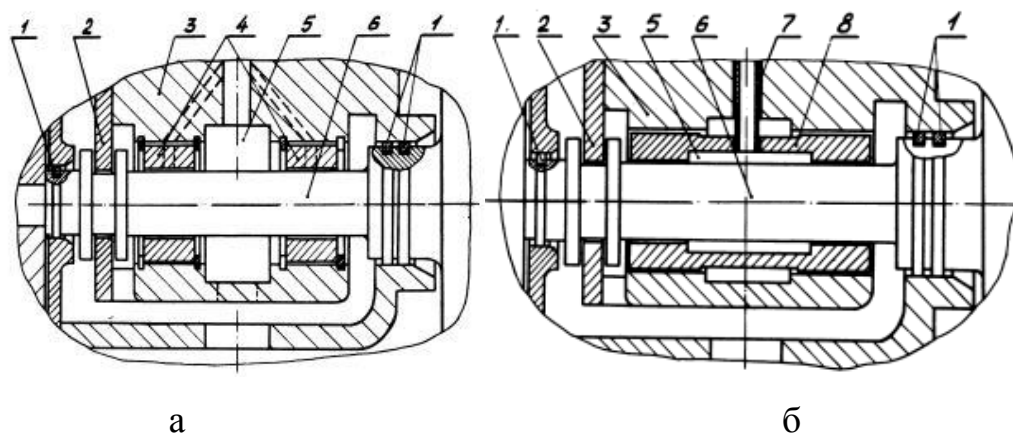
Конструкція підшипникових вузлів а) з плаваючими втулками, що обертаються; б) з плаваючою моно втулкою, що не обертається. 1 - кільця ущільнювачів; 2 - упорний підшипник; 3 - корпус; 4 - плаваючі втулки; 5 - підведення масла; 6 - вал ротора; 7 - стопорна втулка; 8 - плаваюча моно втулка.
